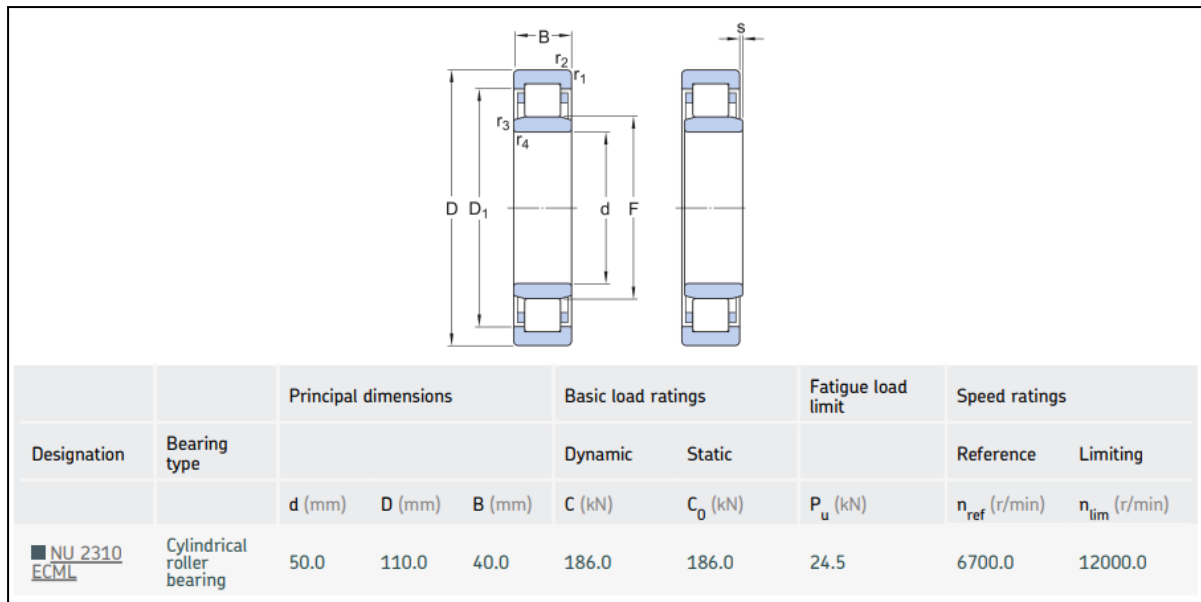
Selección Rodamiento Mecanismo Jansen. [43].
